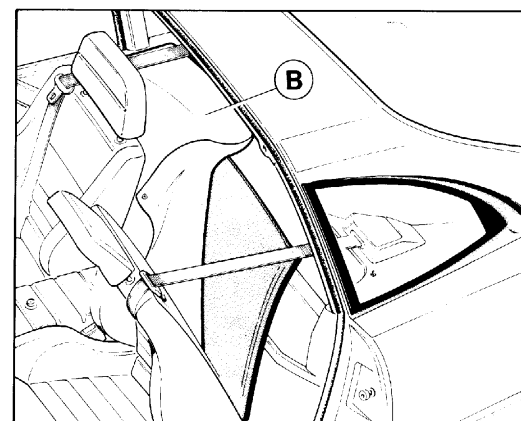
26 - 27 - Capot (démontage et montage)
